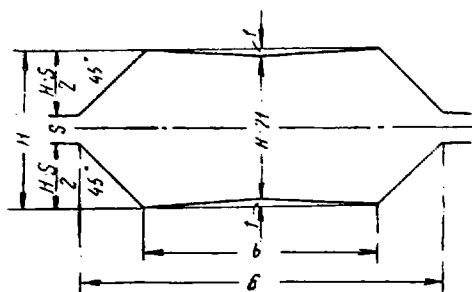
Предчистовой калибр для прокатки шестигранной стали
